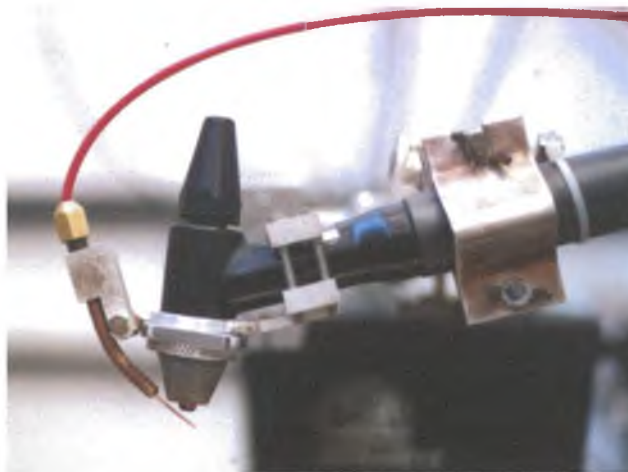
Pistola de Soldagem PLASMA Adaptada
